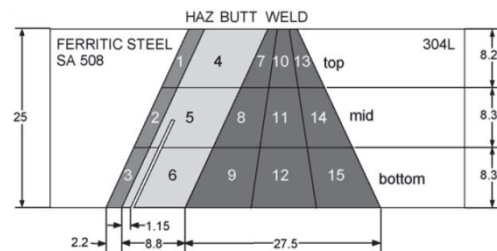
Zones définies à l’intérieur de la soudure bimétallique [SCH 04]
